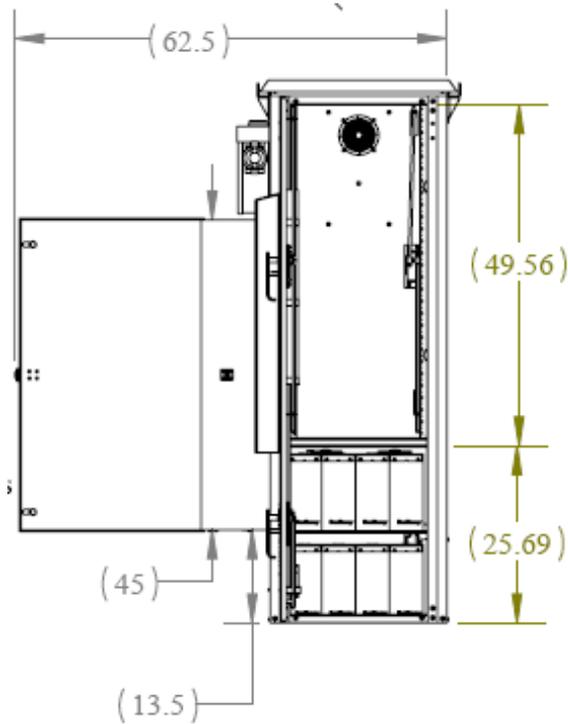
VISTA DIMENSIONAL FRONTAL DEL LTEE-D
